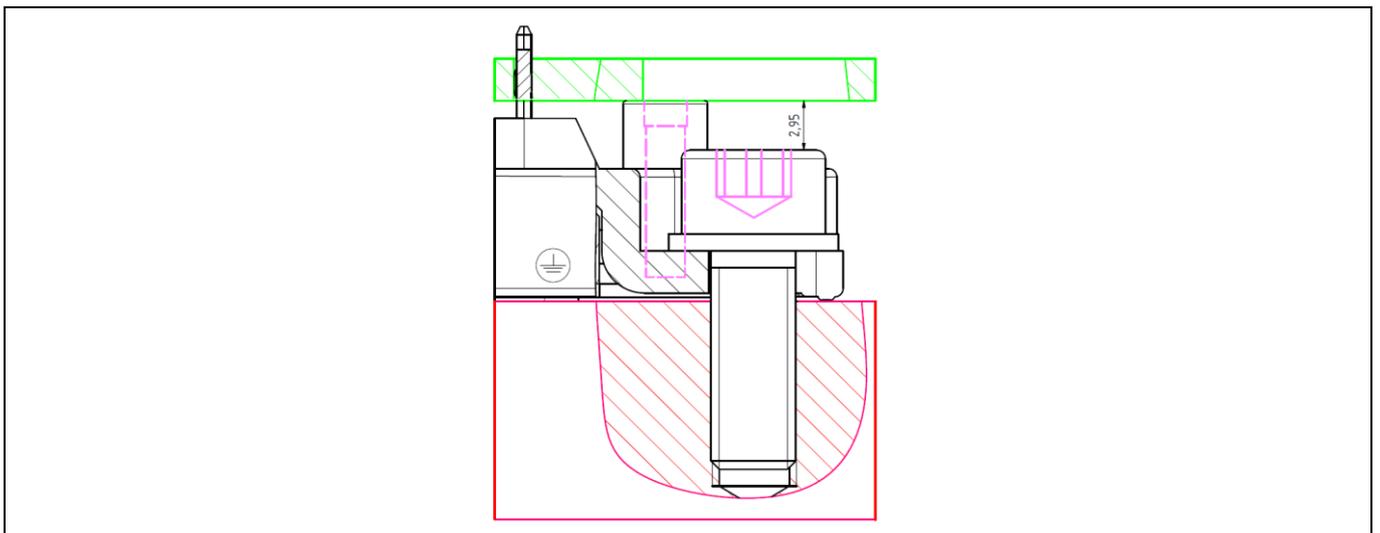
Easy3B 封装的夹具和 PCB 之间的空间距离
